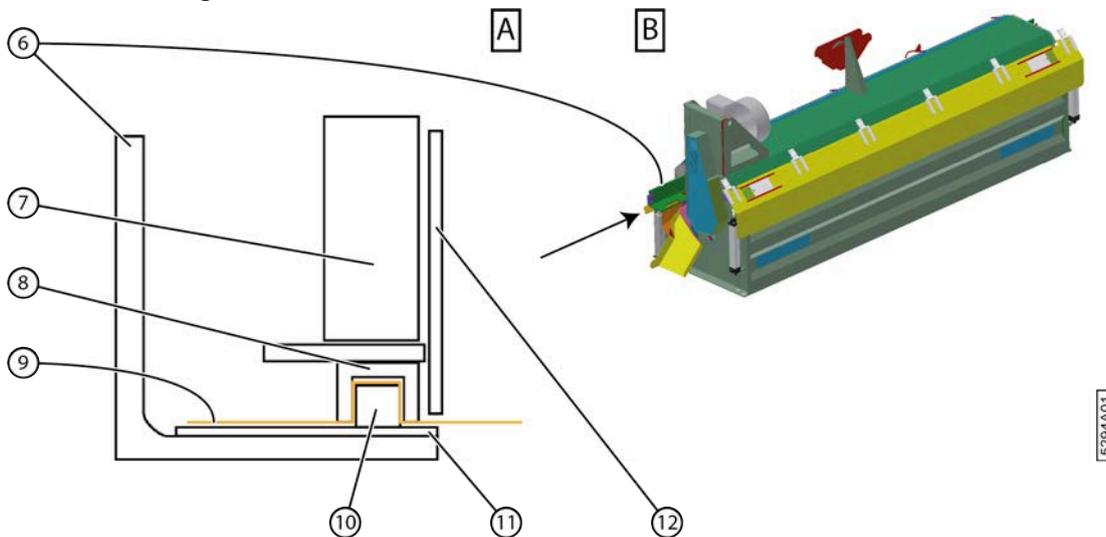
Section transversale [A] d'un tambour de pied [B]
